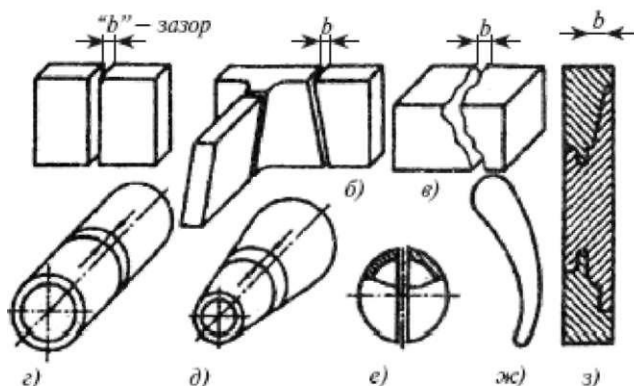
Виды сварных швов: а,б—прямолинейные на вертикальной и наклонной плоскостях; в- участок шва пространственной формы (трещина); г,д,е—кольцевые на цилиндрической, конической и шаровой
